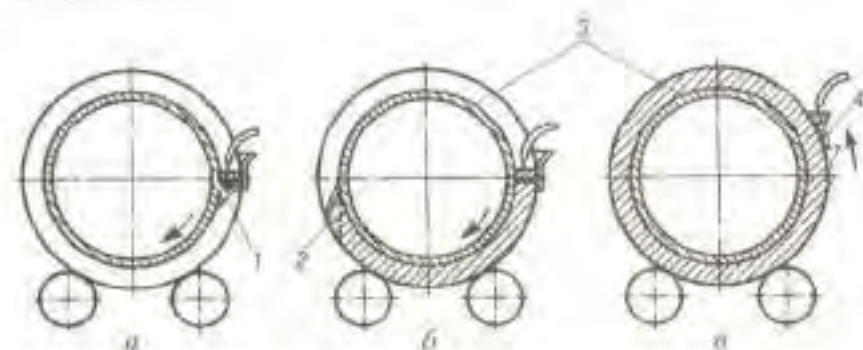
Схема електрошлакового зварювання кільцевих швів:
